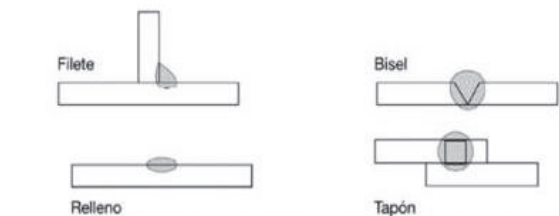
27 Tipos de soldaduras¹⁸
